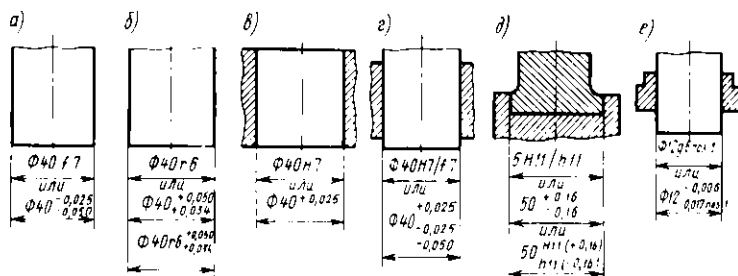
Примеры обозначения полей допусков и посадок на чертеже
